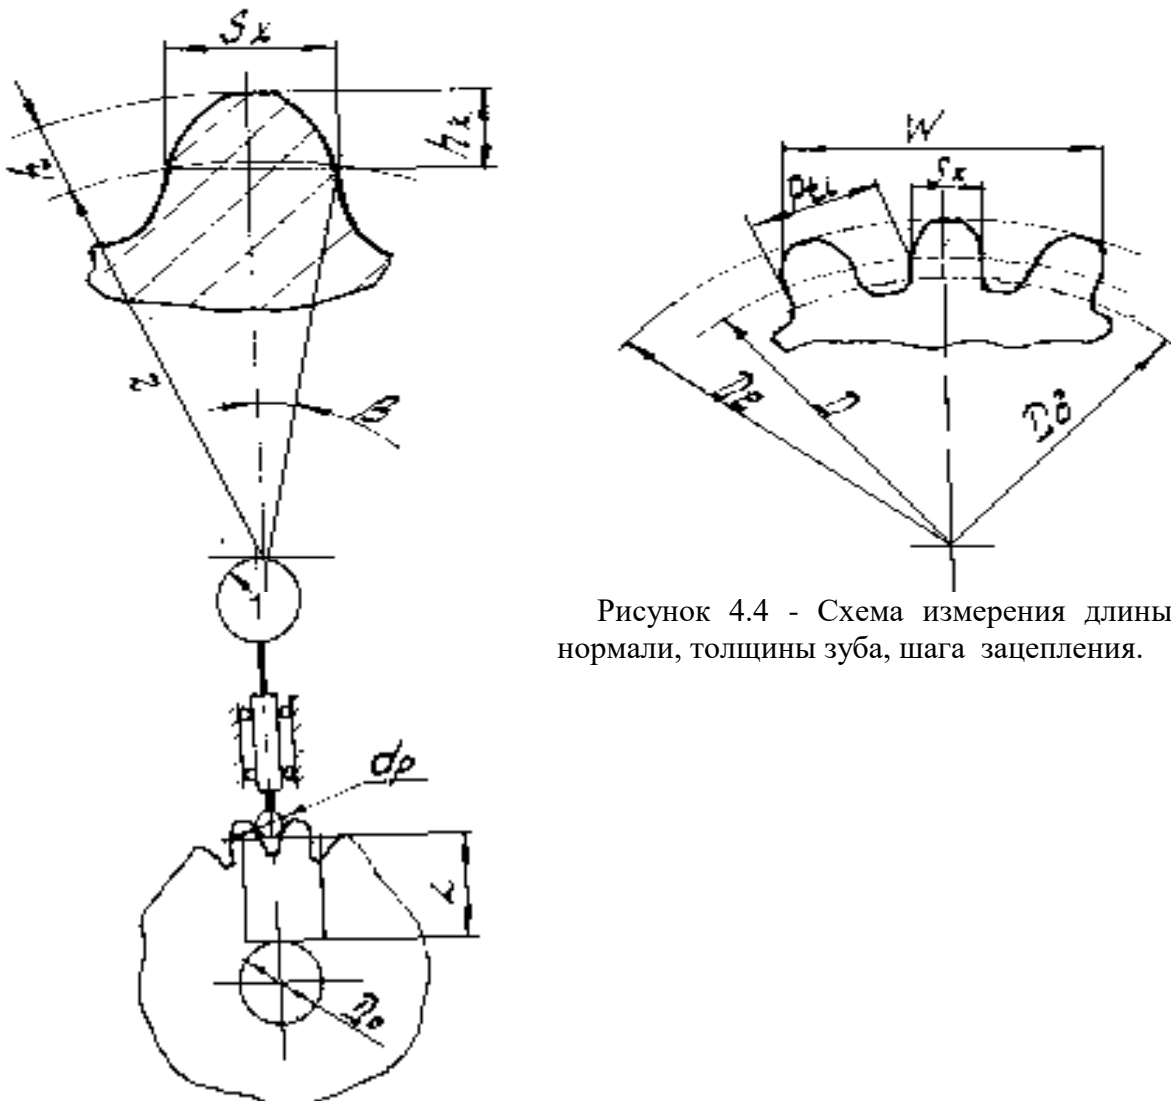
Схема измерения длины общей нормали, толщины зуба, шага зацепления.
